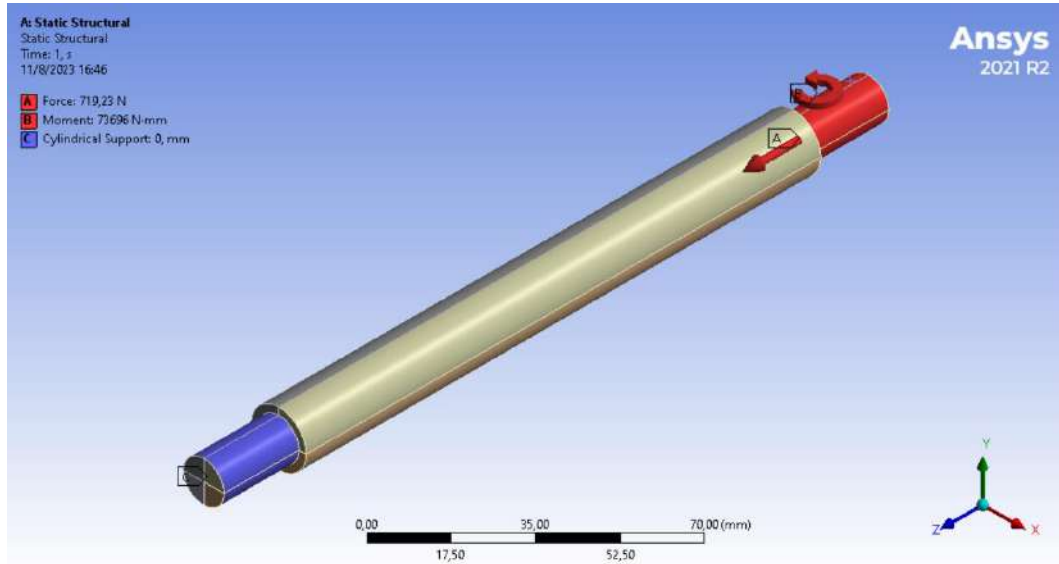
Fuerzas y apoyos aplicados al elemento conductor o biela.
